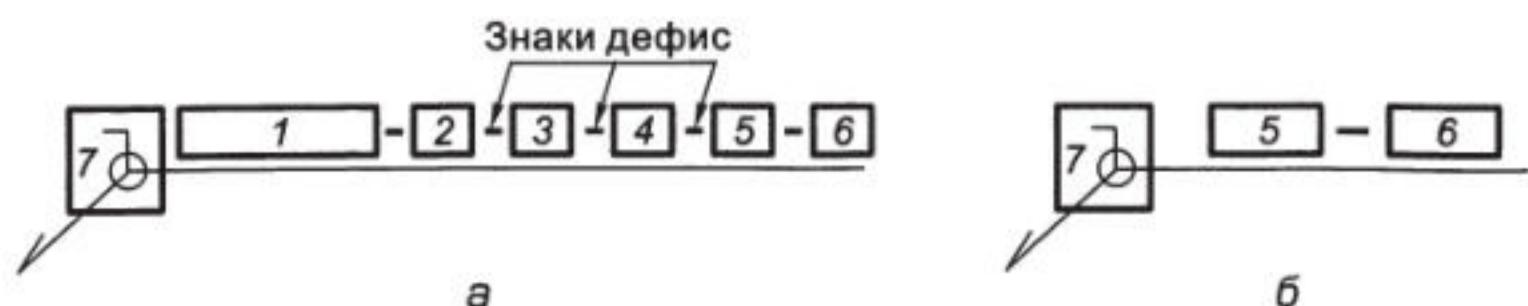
Структура условного обозначения стандартного сварного шва (а), одиночной сварной точки и нестандартного шва (б)
